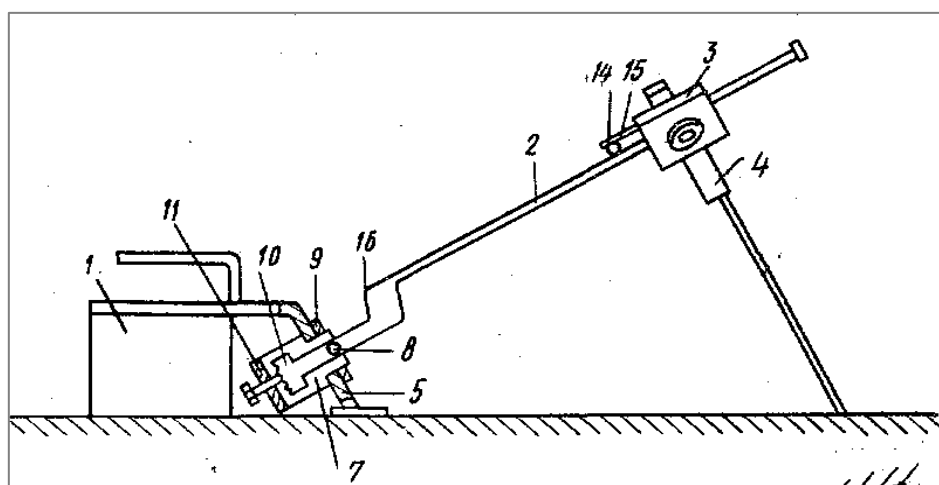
, а – Устройство для сварки наклонным электродом
